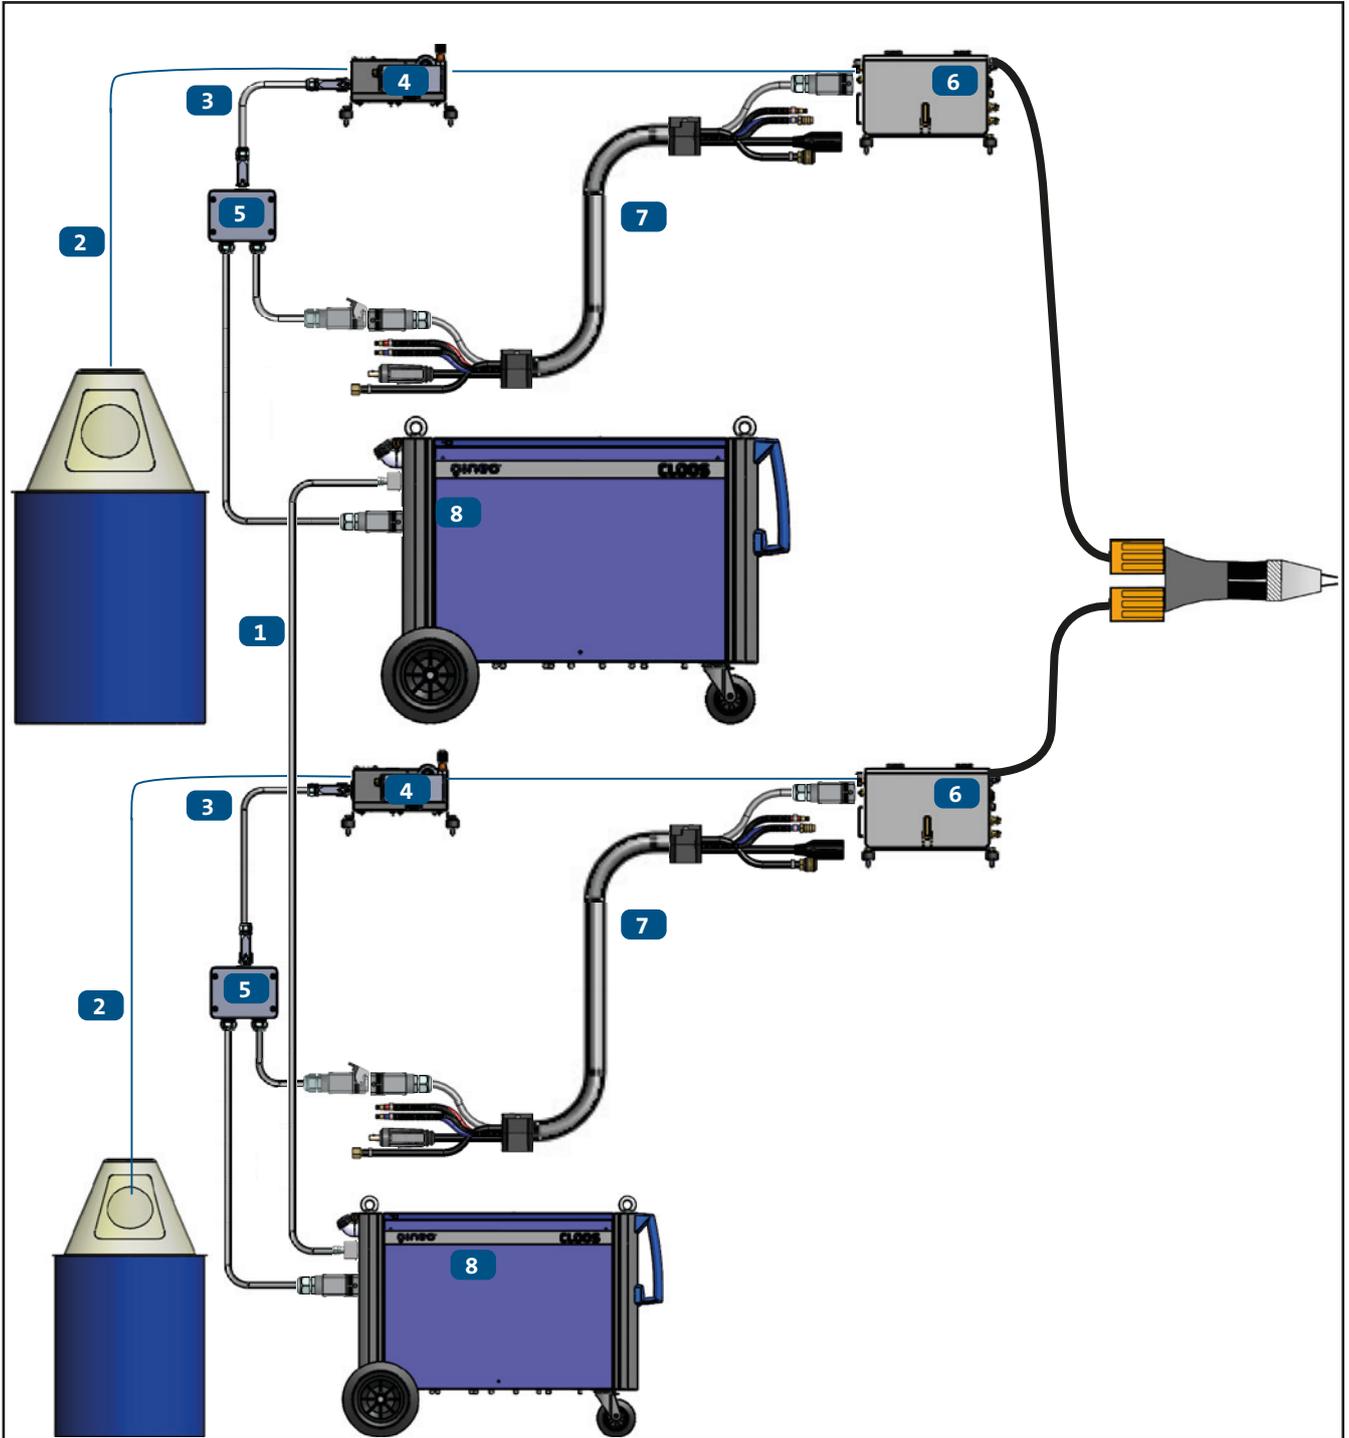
QWD-B Anschlusschema für den Tandemschweißprozess
